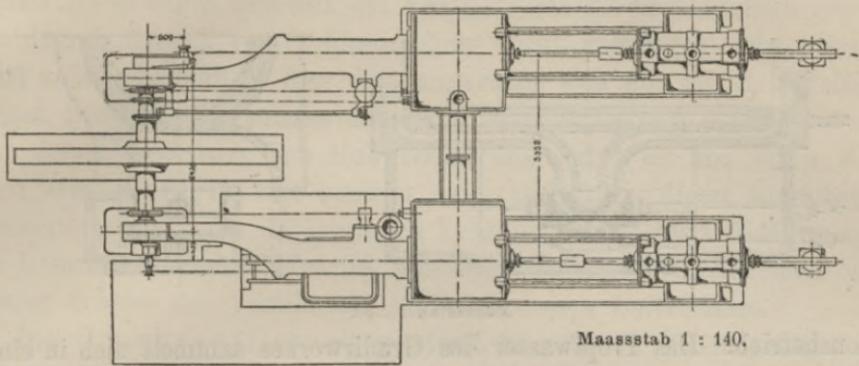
Seitenansicht der Luftkompressionsmaschinen.
